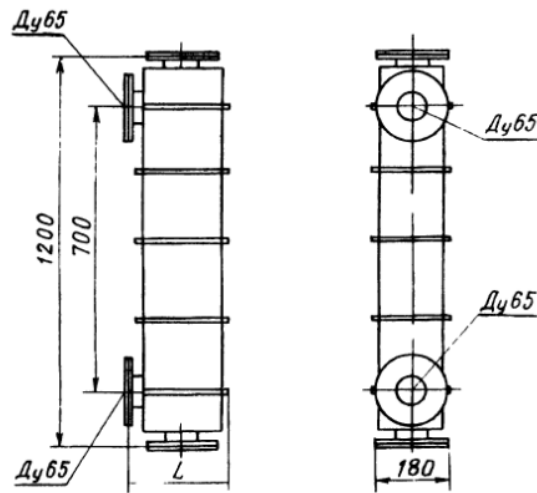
Теплообмінник пластинчастий зварний
